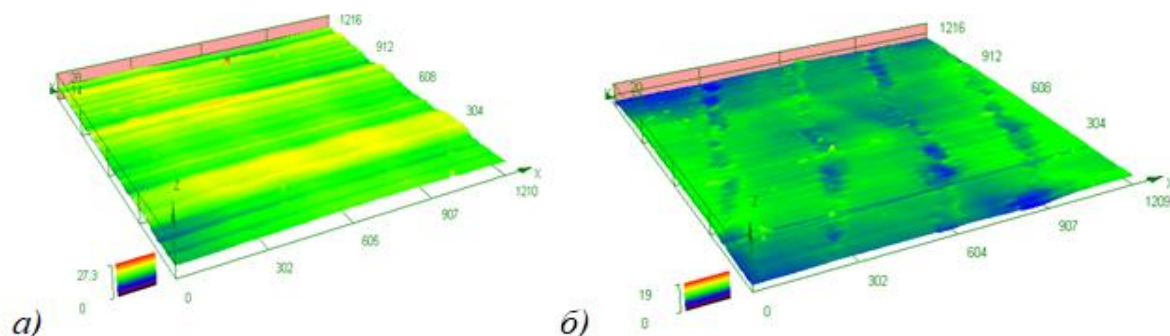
3D распределение высот поверхностного рельефа сплава ВТ22, обработанных фрезами Ø50: а) фрезой, выполненной по ГОСТ 23248-78; б) фрезой с волнообразной режущей кромкой
